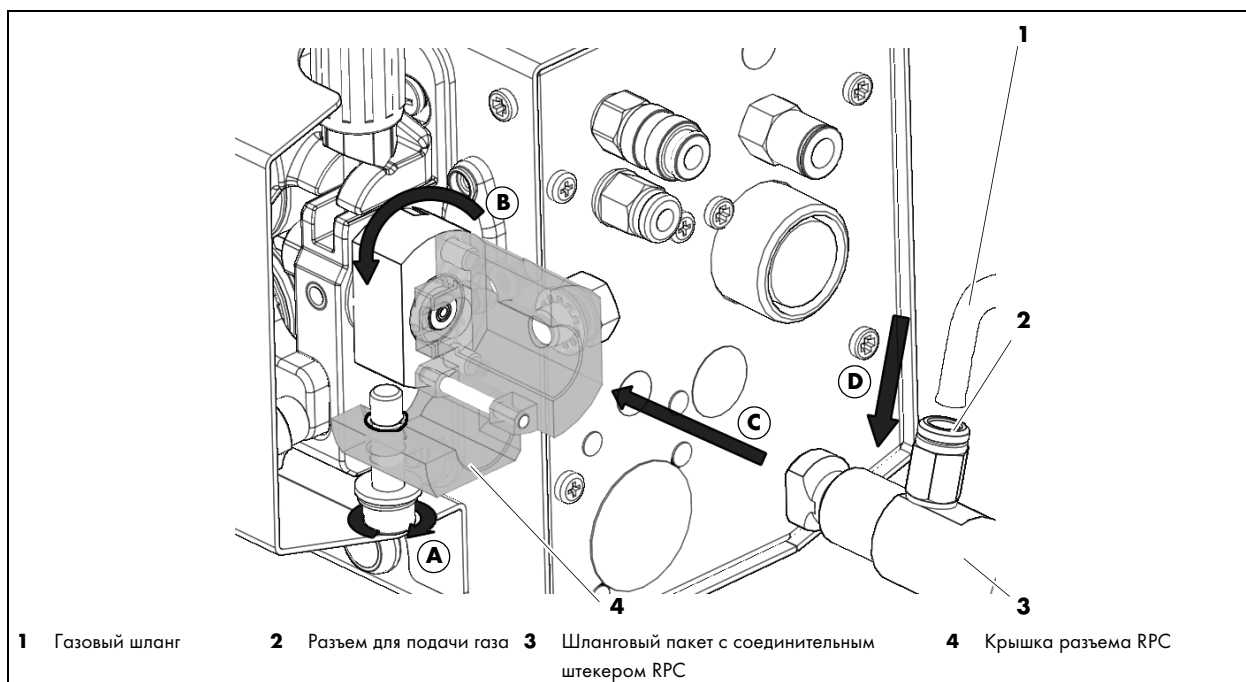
Шланговый пакет сварочной горелки (разъем RPC) iROB-feed 22
